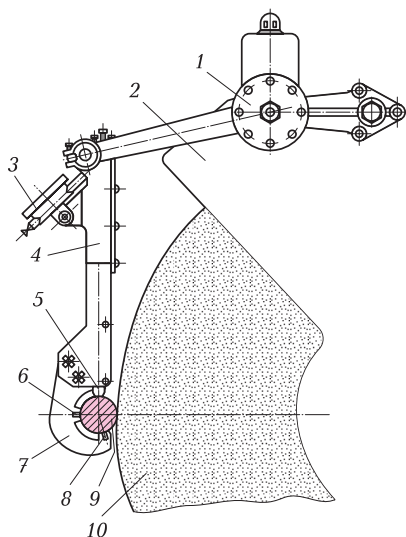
Схема прибора для контроля диаметров валов в процессе шлифования
